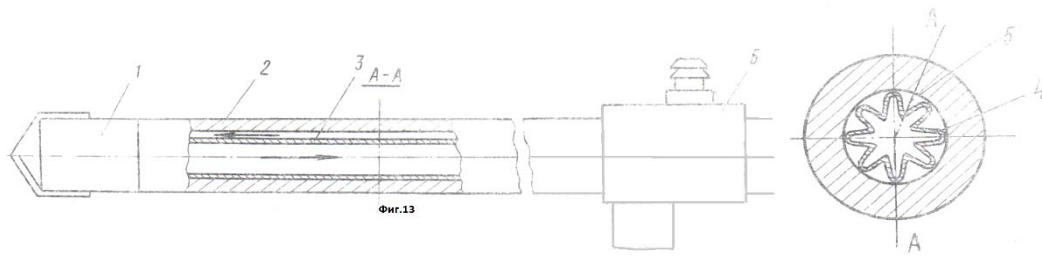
Конструкція ежекторного свердла для гасіння вібрацій
